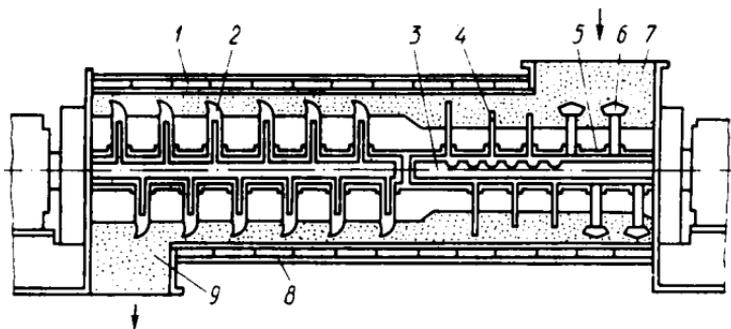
Схема работы высокооборотного смесителя ДСМ-5:
